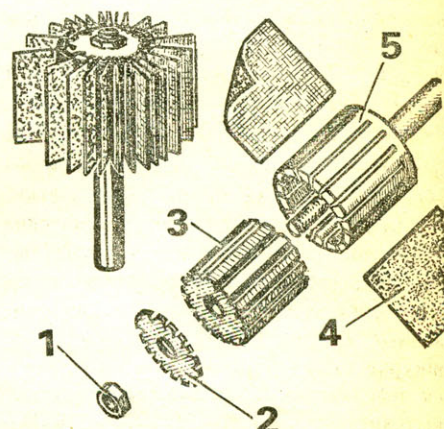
Разъемная щетка: 1 — гайка, 2 — шайба, 3 — резиновый цилиндр, 4 — шкурка, 5 — металлический корпус-стакан.
